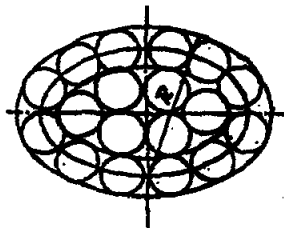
Схема секторной токопроводящей жилы силового кабеля сечением 25-70 кв.мм (до уплотнения)
